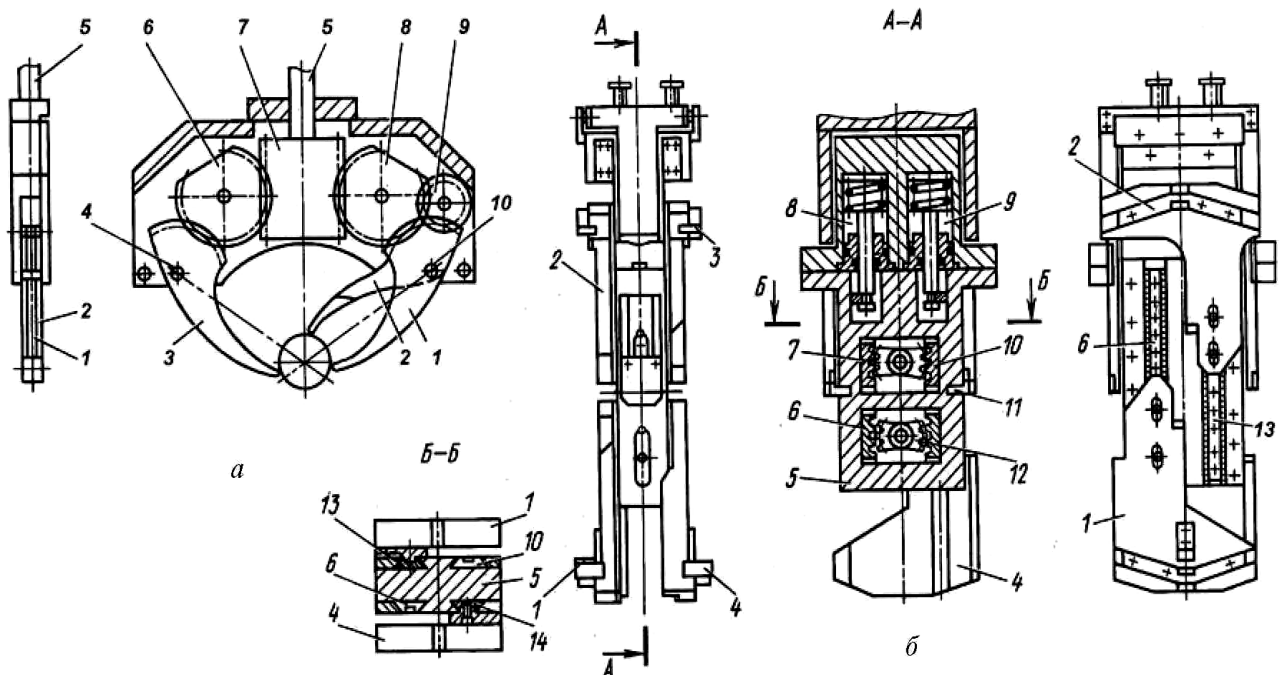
Центруючі ЗП із комбінованими зубчато-рейковими передавальними механізмами:
